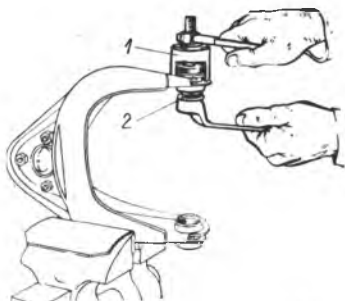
Выпрессовка шарниров верхнего рычага:
